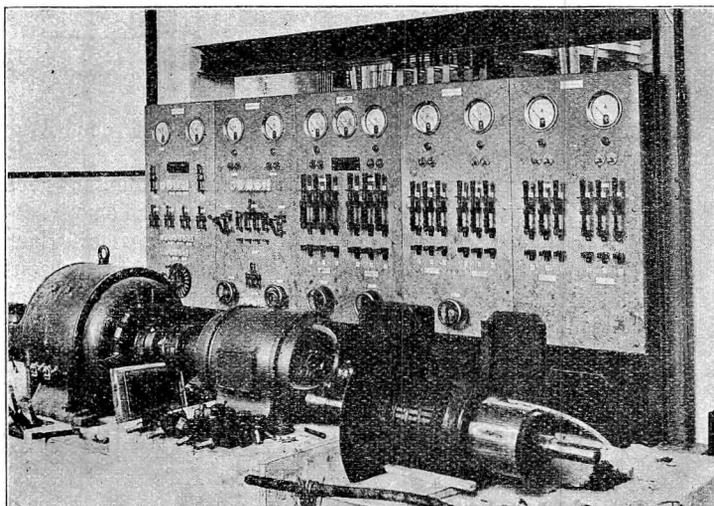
Schweißmaschinensätze und Schalttafel im E. A. W. Ingolstadt.
